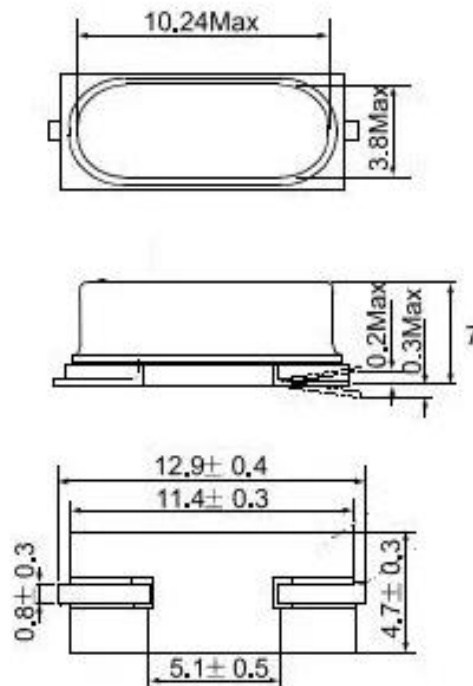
Габаритні розміри кварцового резонатора HS-49SM
